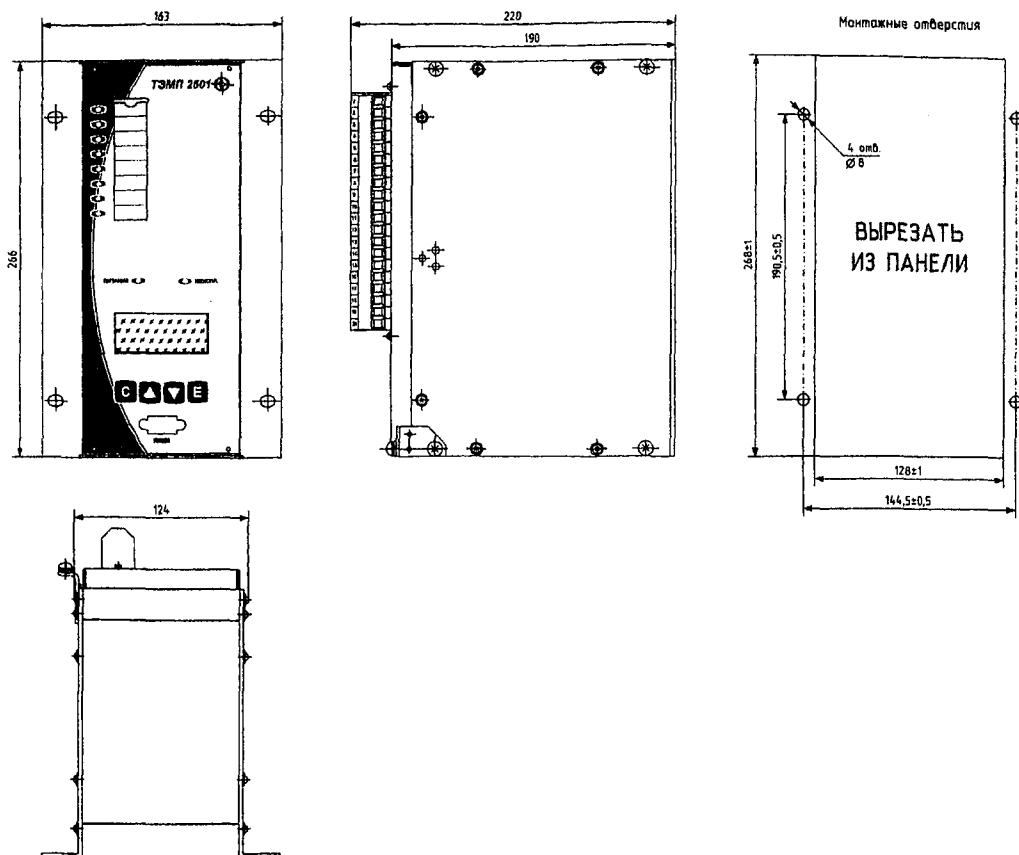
Габаритные и установочные размеры ТЭМП 2501-51/61
